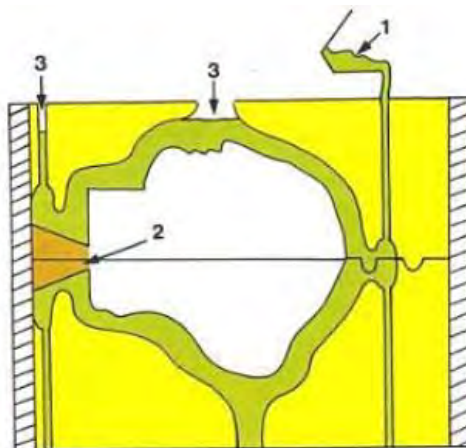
dernière étape de la réalisation du moule à membrane coulée sous chape : coulée du matériau souple. (1 : coulée de la membrane souple, 2 : tige de coulée en terre, 3 : événements)
